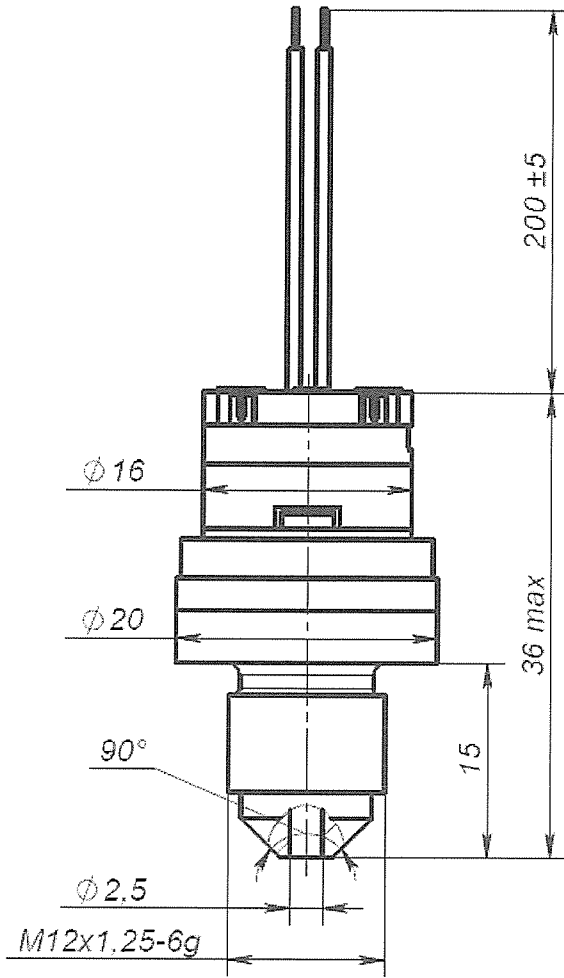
Габаритные и присоединительные размеры тензопреобразователя Д0,1П-1.
